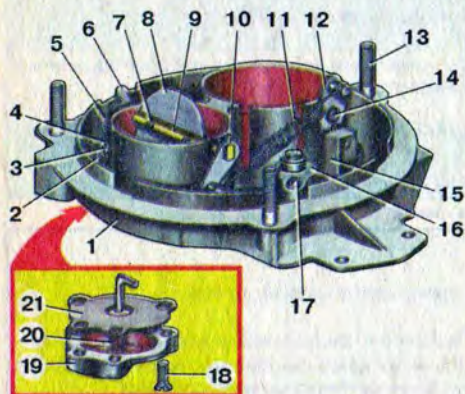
Детали крышки карбюратора: 1 – корпус крышки; 2 – тяга привода воздушной заслонки; 3 – шайба; 4 – шплинт; 5 – секторный рычаг; 6 – промежуточный рычаг; 7, 14, 17, 18 – винты; 8 – воздушная заслонка; 9 – ось воздушной заслонки; 10 – рычаг оси воздушной заслонки; 11 – оттяжная пружина воздушной заслонки; 12 – рычаг регулировки оттяжной пружины воздушной заслонки; 13 – шпилька крепления воздушного фильтра; 15 – стойка крепления рычага устройства разбалансировки поплавковой камеры; 16 – крышка балансировочного канала; 19 – крышка диафрагменного механизма пускового устройства; 20 – пружина диафрагмы; 21 – диафрагма
